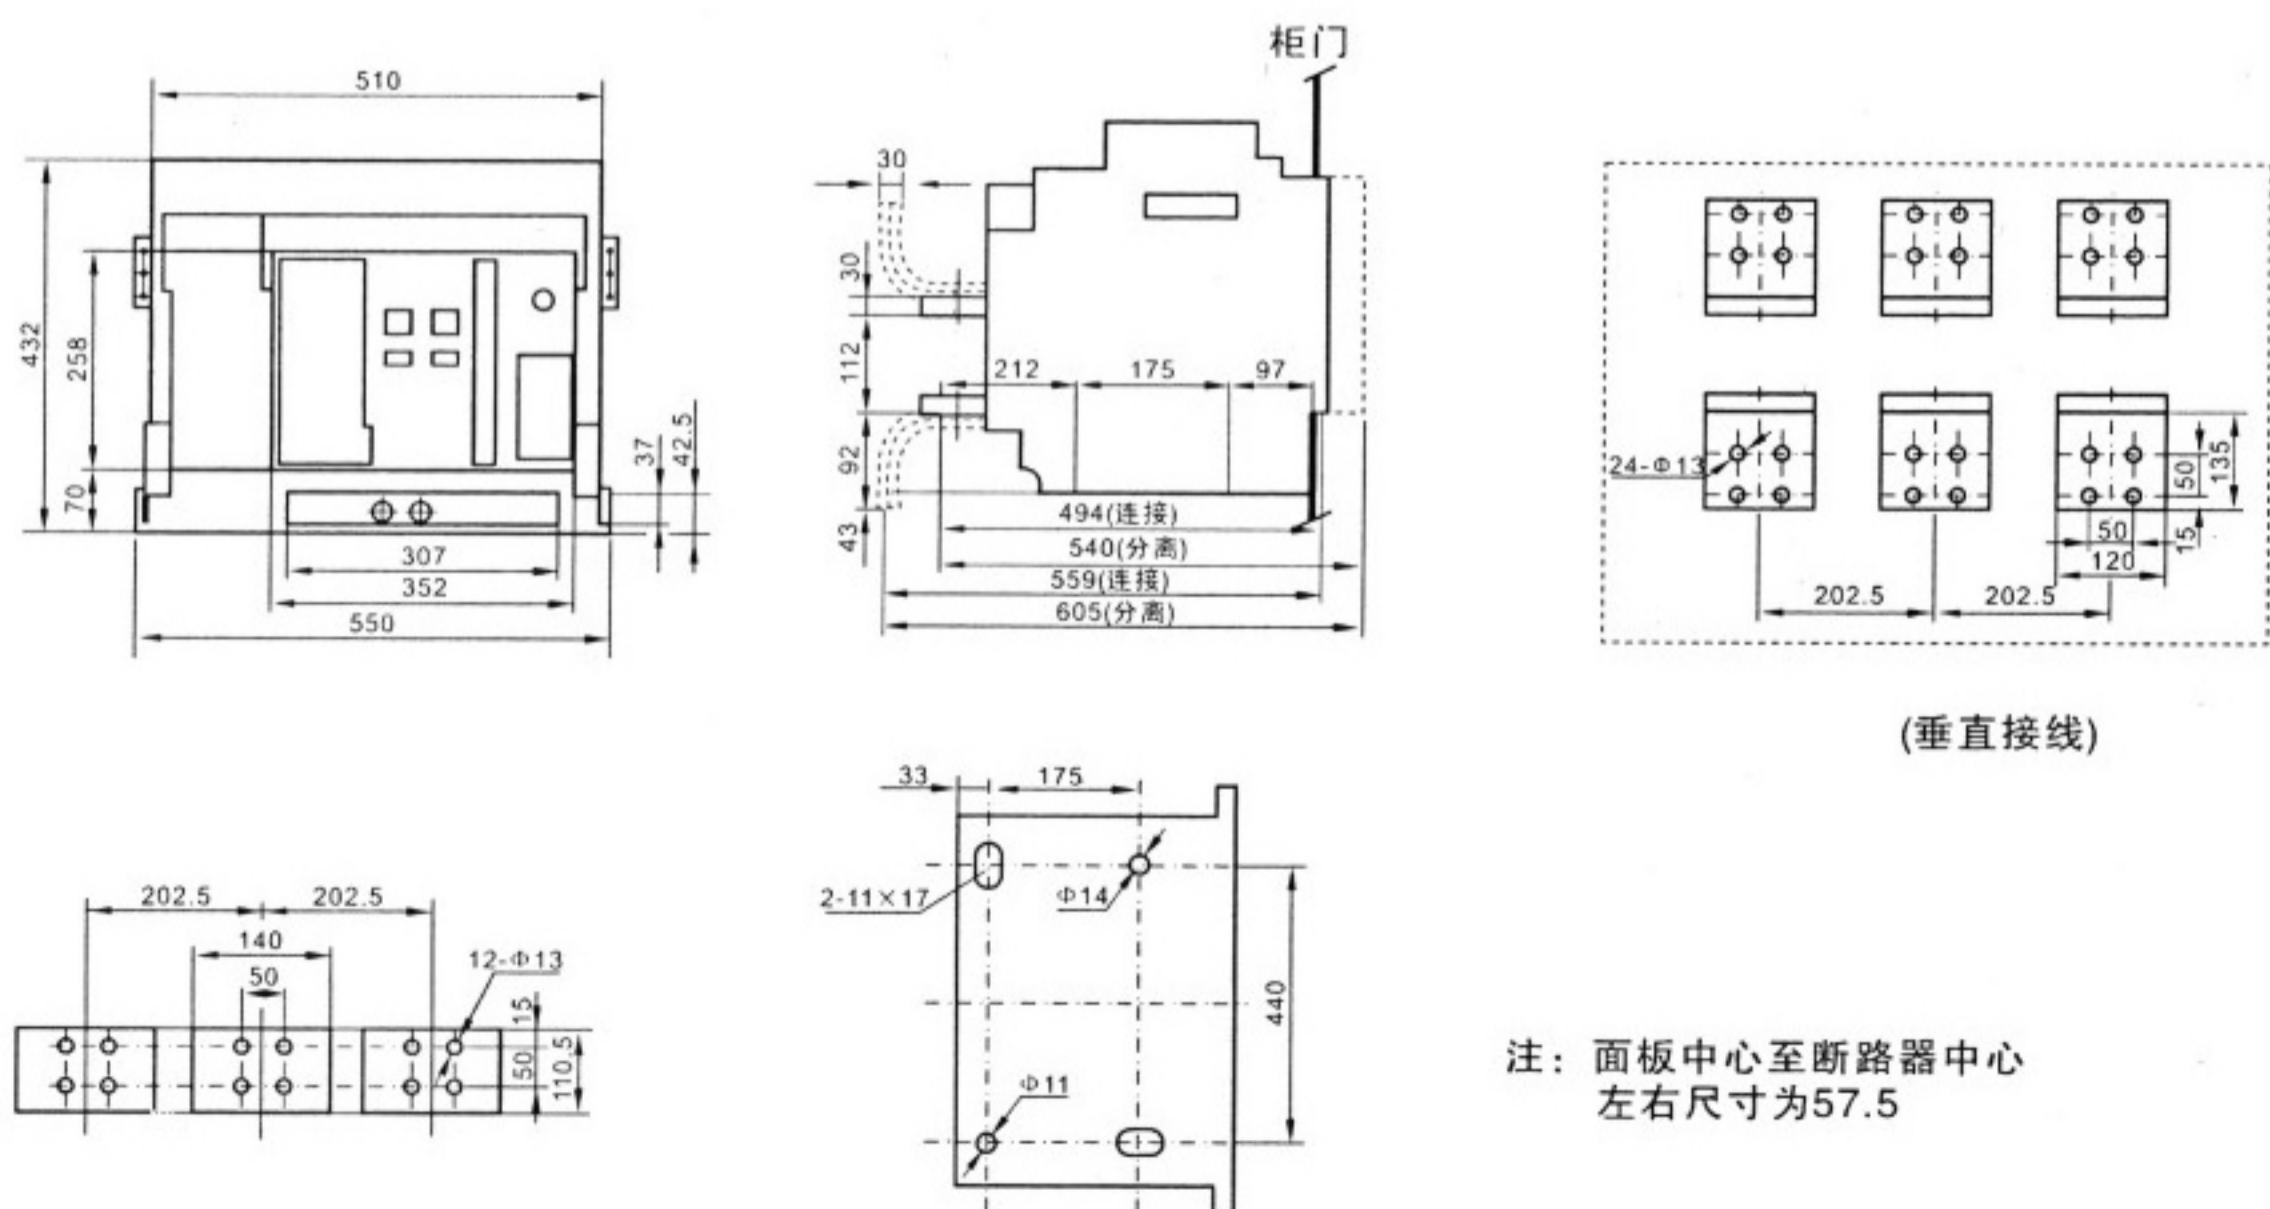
抽屉式断路器安装尺寸及外形尺寸(4000)
